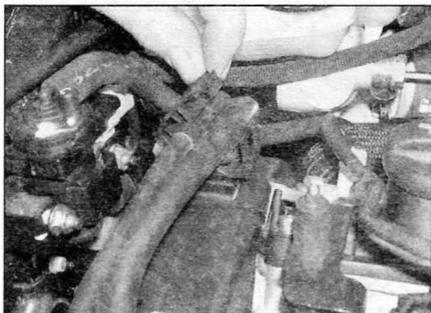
Высвободите два шланга из зажимов на верхней крышке ремня газораспределительного механизма (двигатели 2.0 л)
